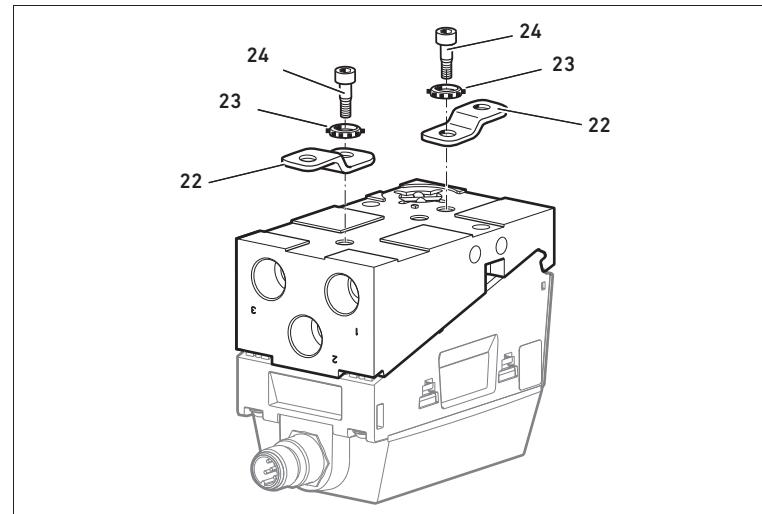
Montaggio del set di fissaggio per piastra di montaggio
